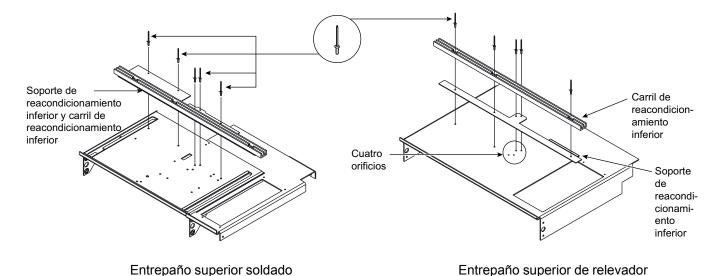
Ensambles de estante superior soldado y de relevador
